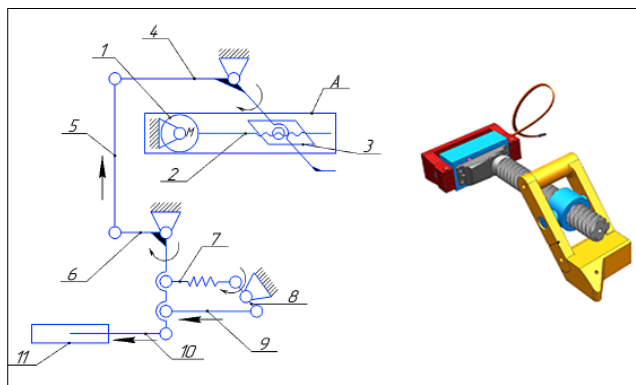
Мехатронный модуль привода управления системы включения сцепления: 1 – сервопривод; 2 – винт; 3 – гайка с шарниром; 4, 6, 9 – коромысла; 5, 8 – шарниры; 7 – пружина; 10 – шток; 11 – пневмоцилиндр; А – мехатронный модуль воздействия
